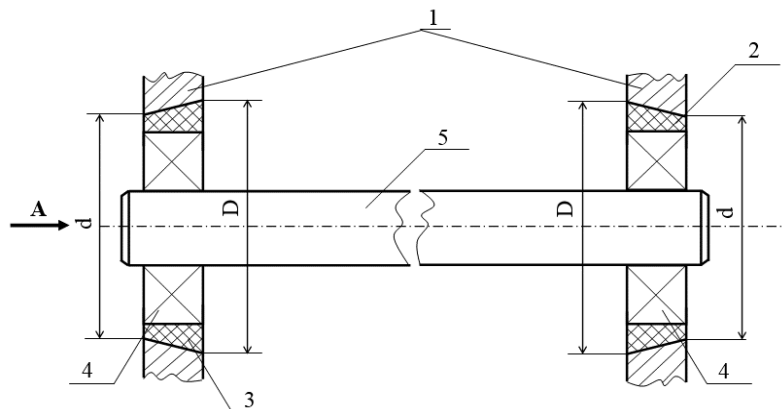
Схема установки вала на опорах с упругими усеченными коническими втулками
